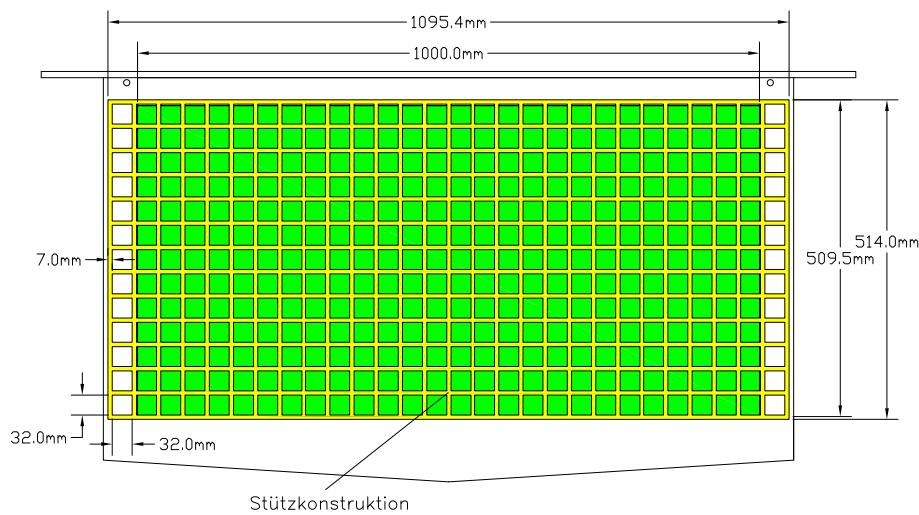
Frontansicht Austauschfläche mit Stützkonstruktion
